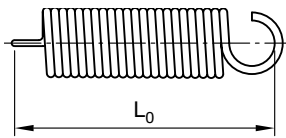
edZ) Zylindrische Schraubenfeder (Zugfeder)
